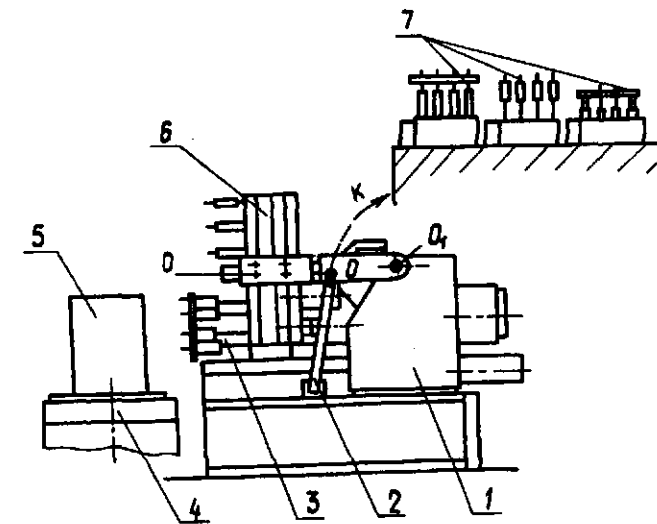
Схема переоснащения агрегатной силовой головки 1 сменными многошпиндельными коробками с двумя поворотными устройствами
